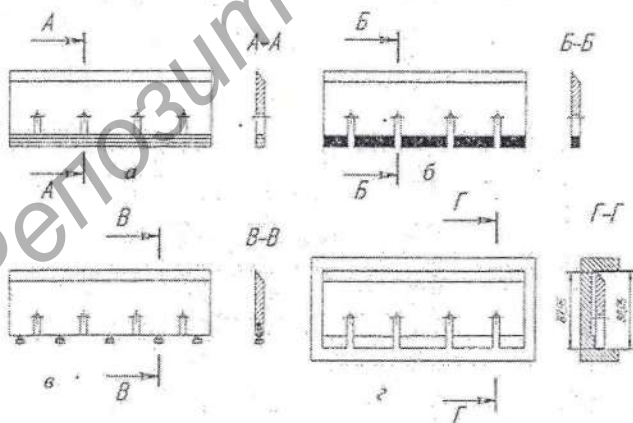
Рубильные ножи: а — тип 1; б — тип 2; в — тип 3; г — шаблон-калибр для контроля установочной ширины ножей
